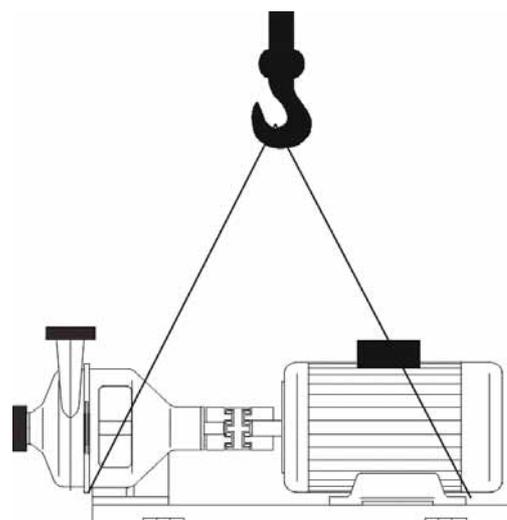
Anschlagpunkte für CN Pumpe (Beispiel)
